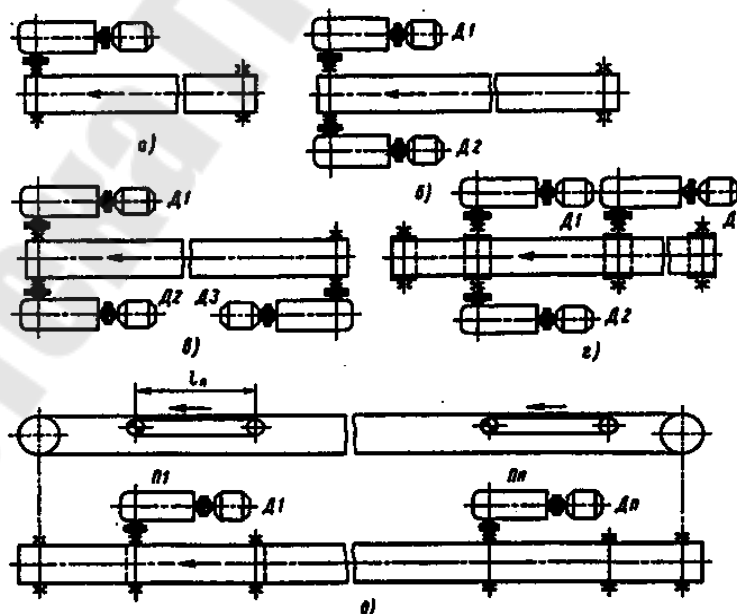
Схемы расположения приводов а - однодвигательного; б - двухдвигательного; в и г - трехдвигательных; д - многоприводного с прямолинейными промежуточными приводами; П - привод; Д - двигатель
